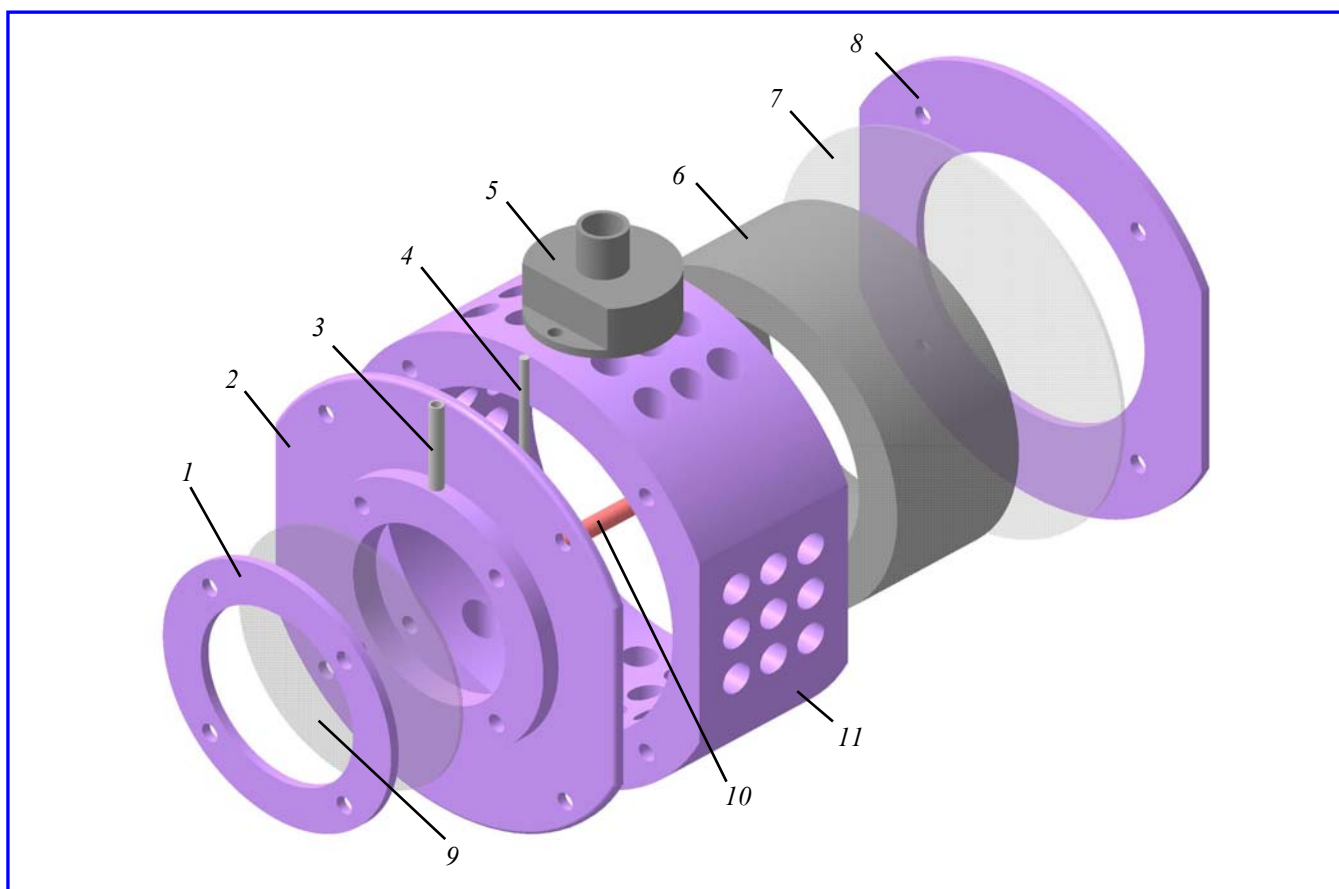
Сборка: 1, 2, 8 – крышка; 3 – патрубок; 4 – держатель; 5 – шток; 6 – пористое тело; 7, 9 – стекло смотрового окна; 10 – нагреватель; 11 – корпус
